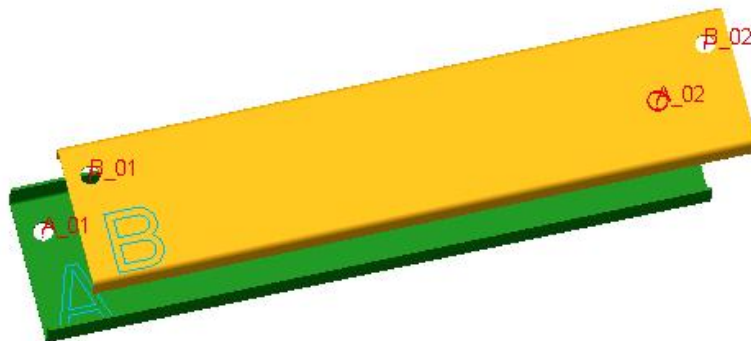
Diámetros A_01, A_02, B_01 y B_02 en partes desensambladas. Vista isométrica.
